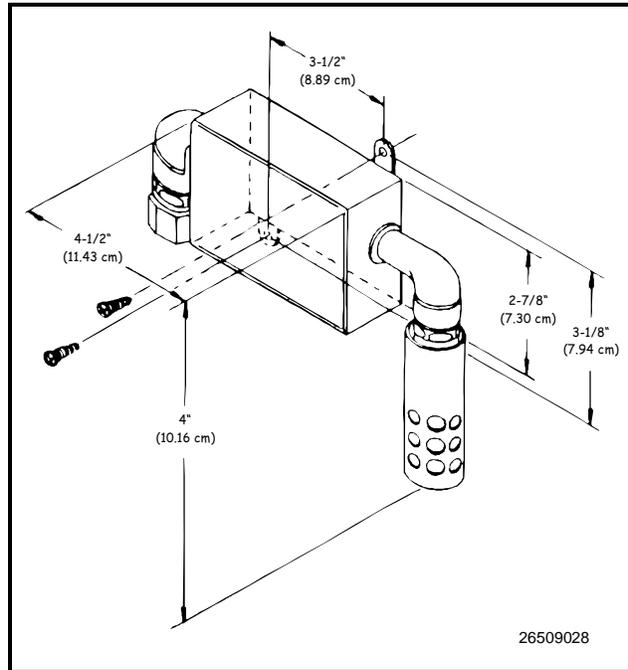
Dimensiones de Montaje del Sensor RH de Exterior
